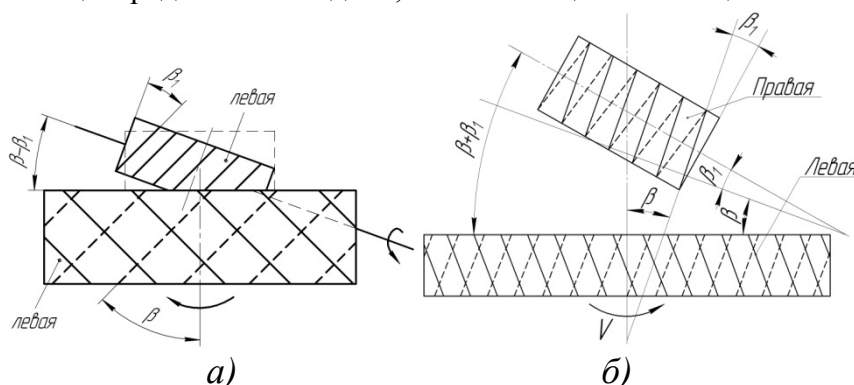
Нарезание косых зубьев на цилиндрическом колесе: а – направления витков фрезы и заготовки одинаковые; б – направления витков фрезы и заготовки разные
